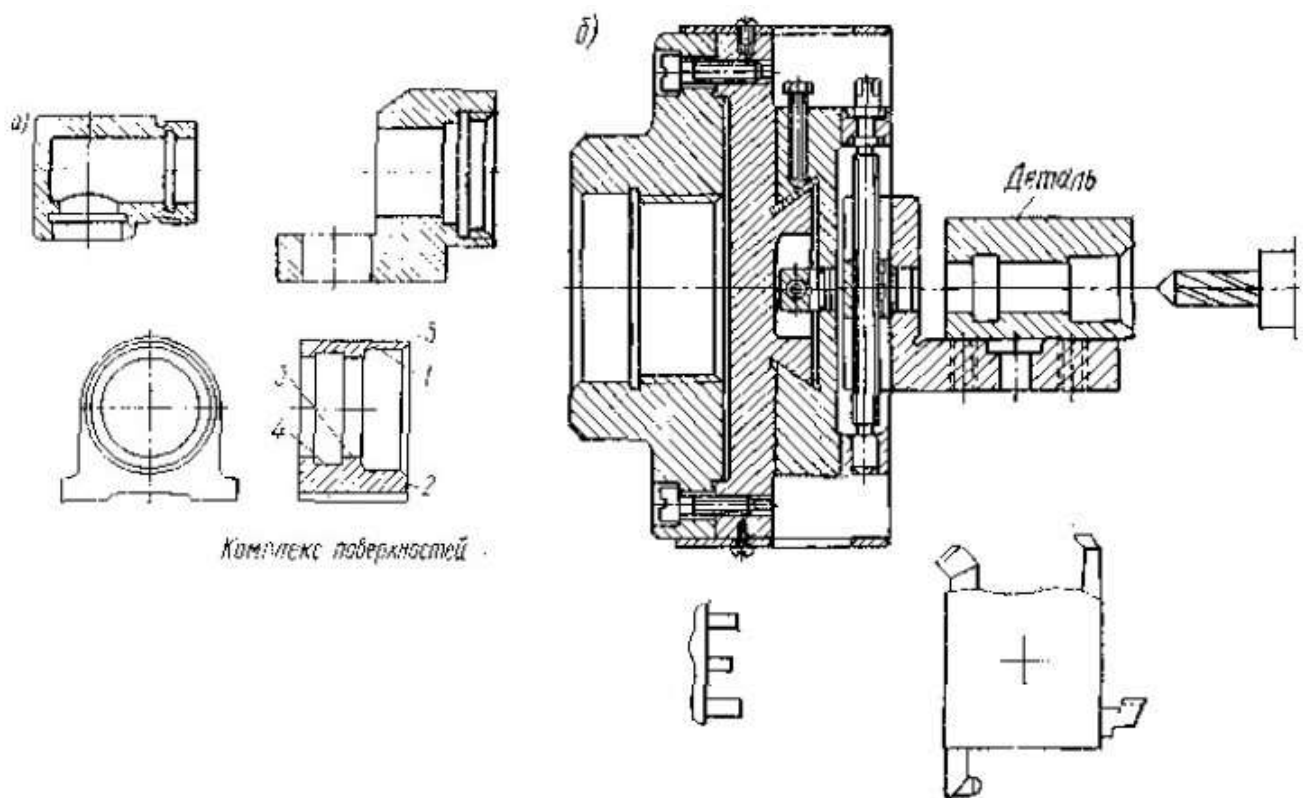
Група деталей і групова оснащення токарного верстата
